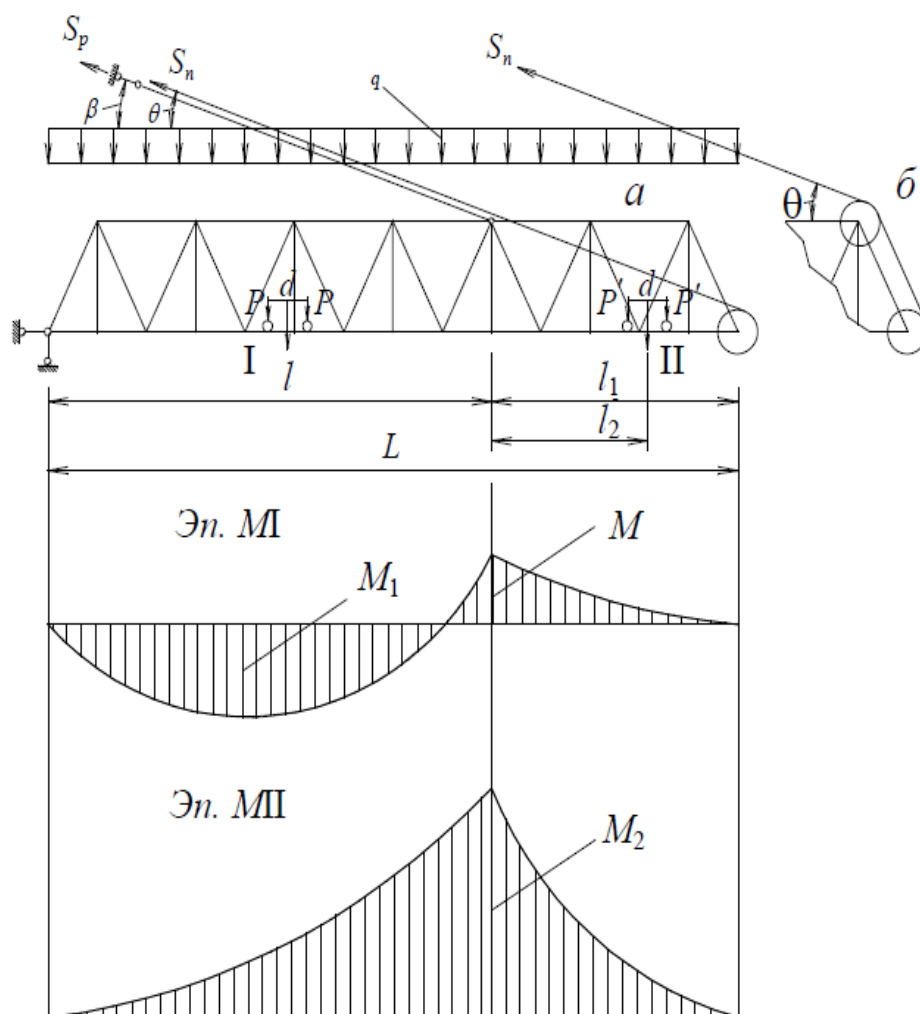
Схема к расчёту нагрузок на стрелу и эпюры изгибающих моментов в вертикальной плоскости:
